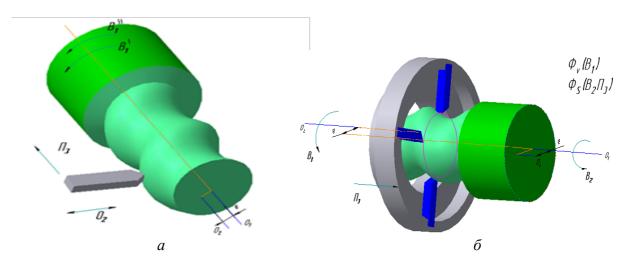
Кинематические схемы обработки круговых винтовых поверхностей на токарно-затыловочном станке
